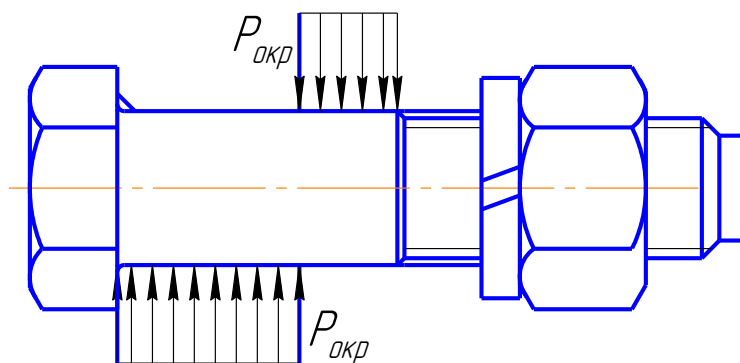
Розрахункова схема болта кріплення обичайки з маточиною.
